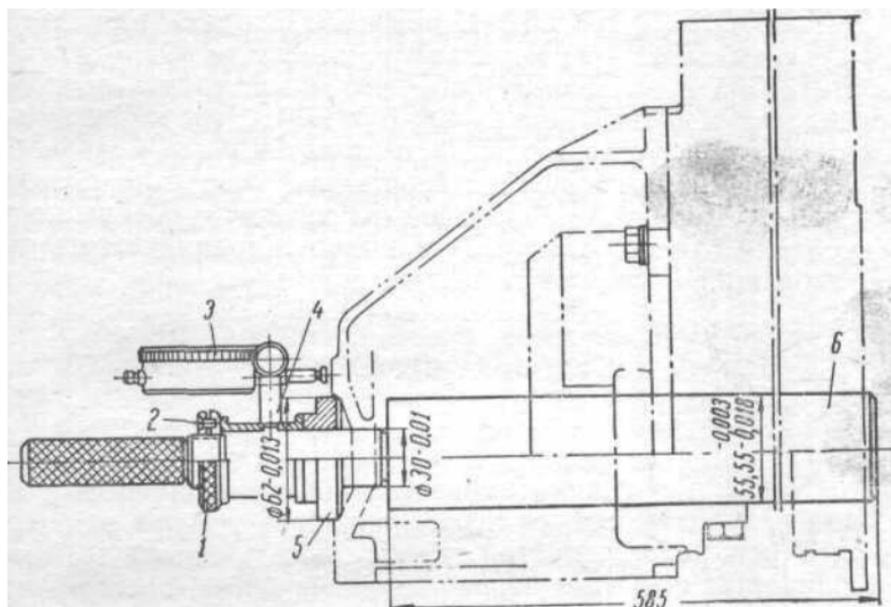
Приспособление для центрирования картера сцепления с блоком цилиндров:
